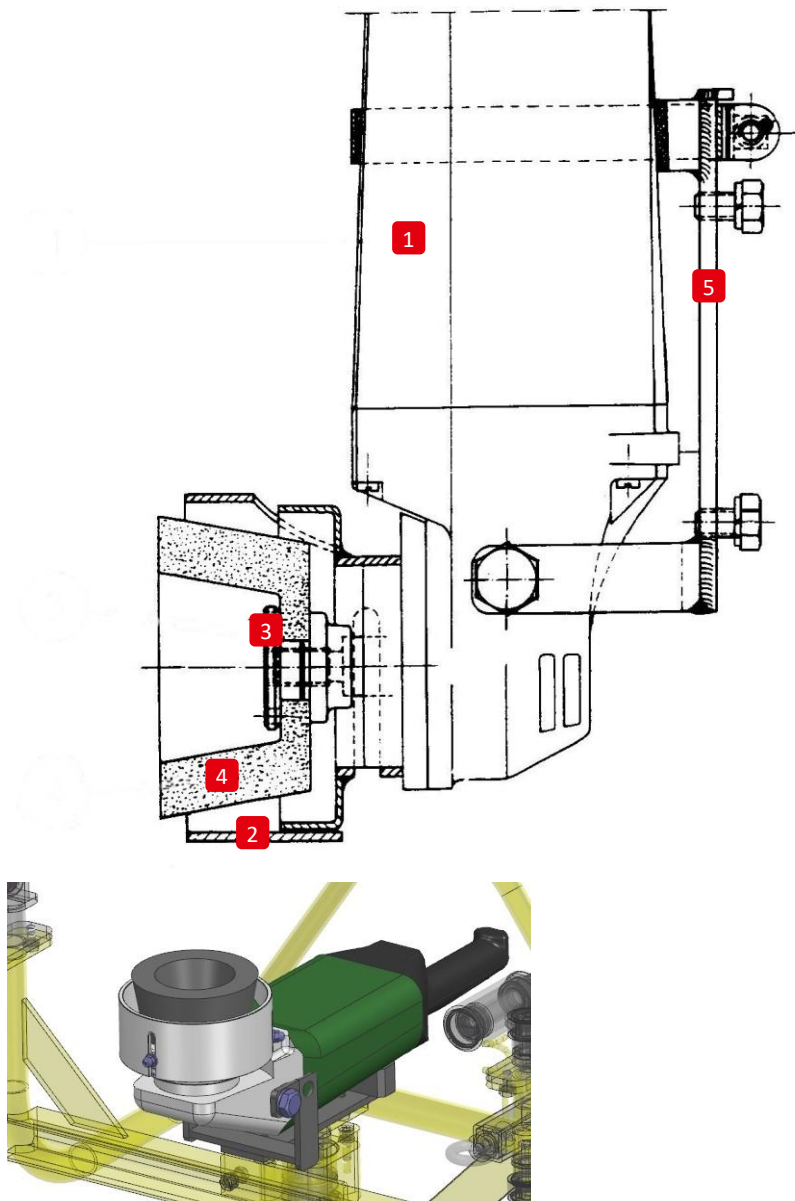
Juego de montaje para la amoladora angular universal y soporte para amoladora angular
